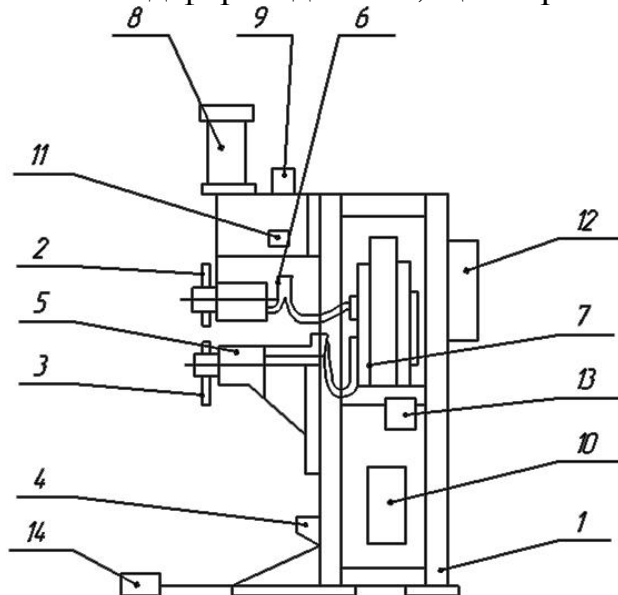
Схема машини типу МТ1215 для точкового контактного зварювання.
